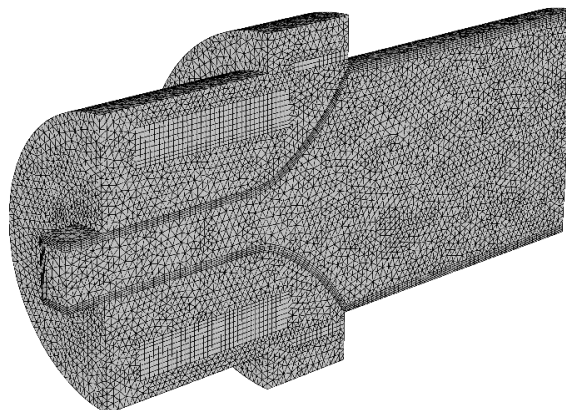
Дискредитована модель пресового інструменту для формування великогабаритних вуглецевих заготовок
